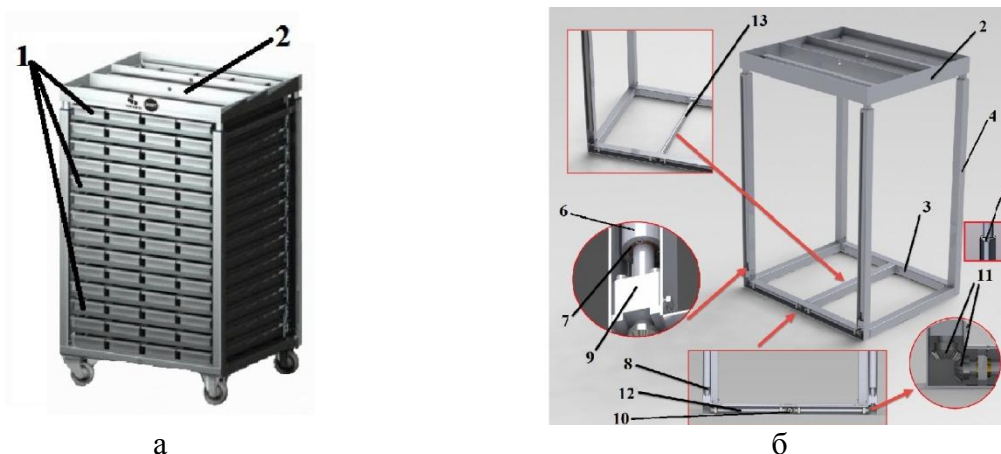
Конструкция башни для термической обработки изделий: а – общий вид башни; б — конструкция механизма подъема-опускания стеллажей
